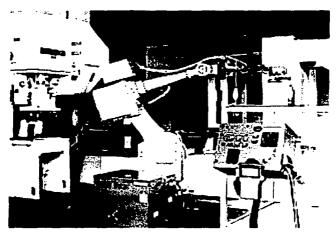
Robot manipulador cambiador de piezas y/o herramientas
